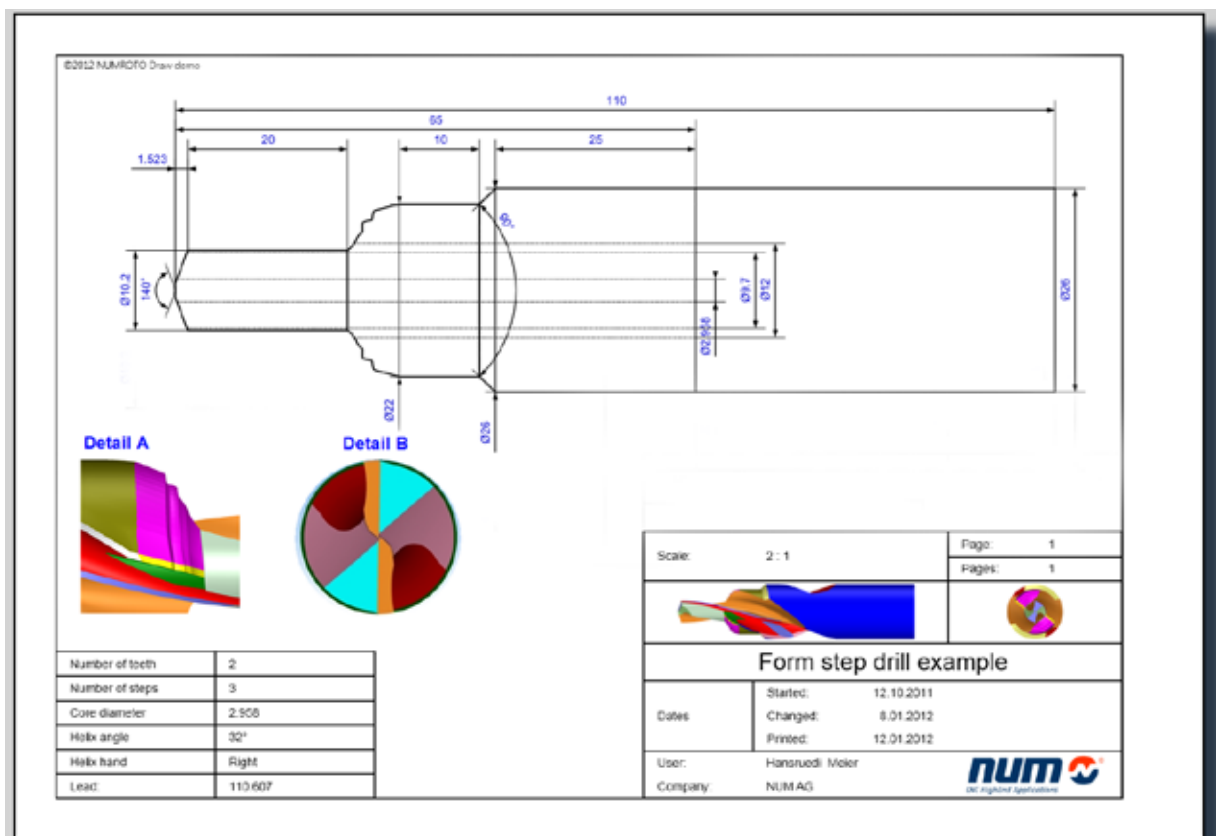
Werkzeugzeichnung eines Stufenbohrers
